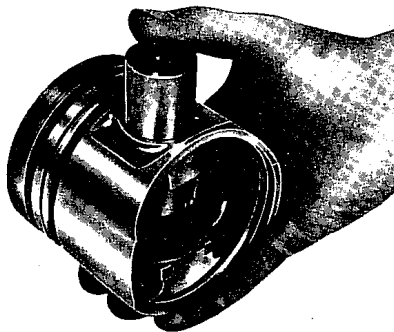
Controllo del giuoco fra le estremità di un anello elastico mediante calibro a spessori A. 395113.
